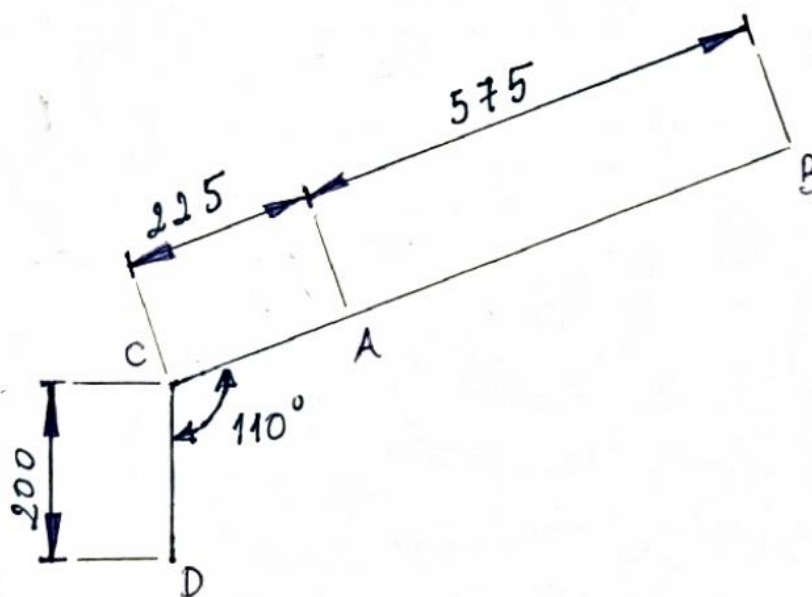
Configuração geométrica do dispositivo e dimensões gerais da haste.
